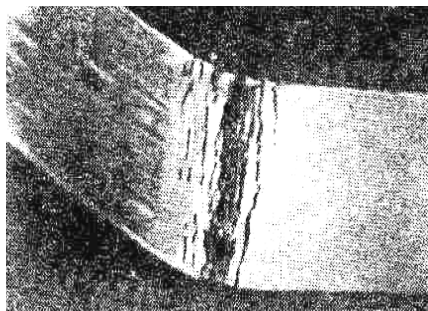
Сварной образец нержавеющей стали, склонной к межкристаллитной коррозии
